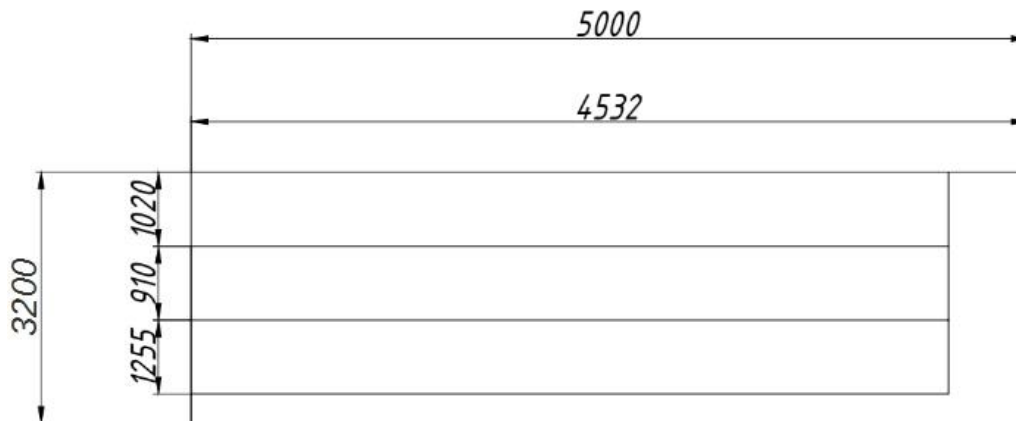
Ескіз розкрою заготовок обічайки на листі
